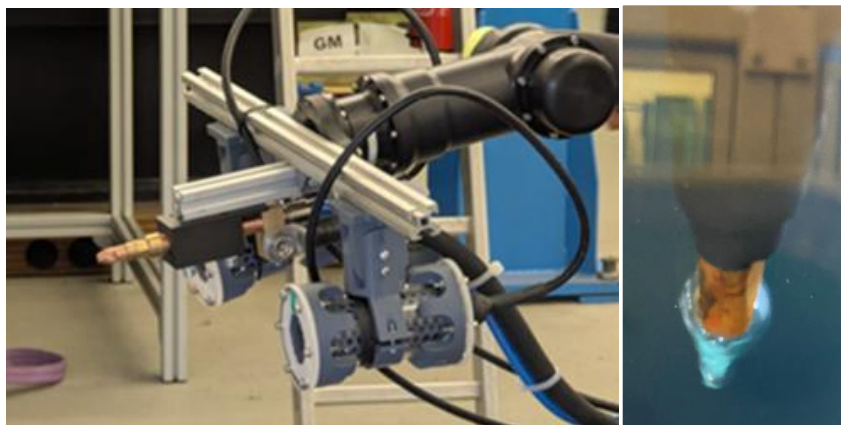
Links: Fülldrahtbrenner im Roboterarm-geführten Schweißprozess;
